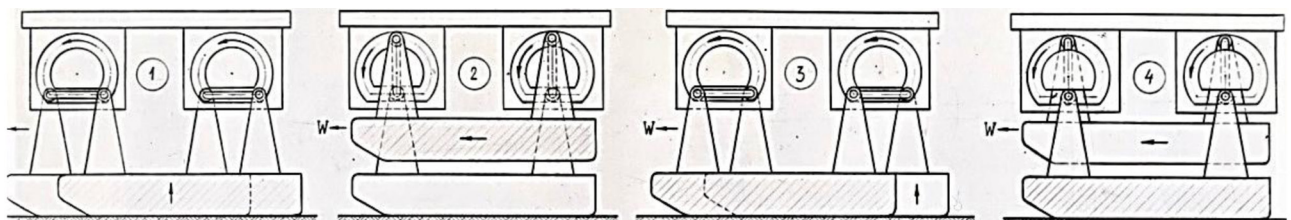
Схемы процесса передвижения шагающего механизма Н.Н. Кокуева с передними и задними направляющими подковообразной формы [19]
